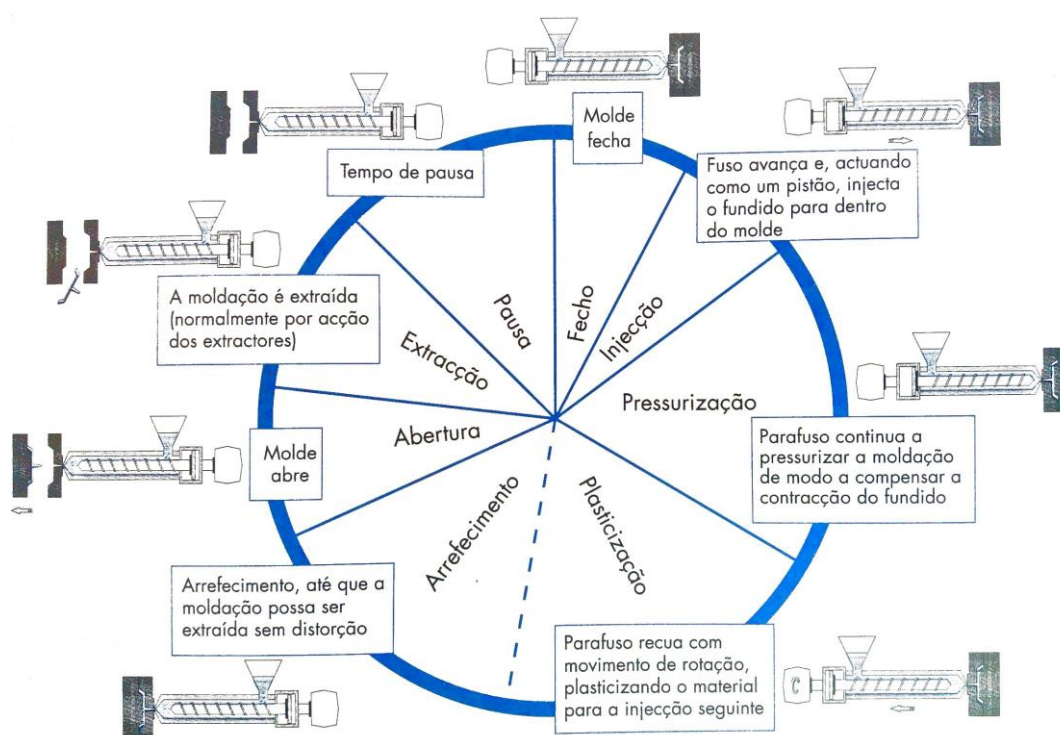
Ciclo de moldação. Adaptado de [20]
